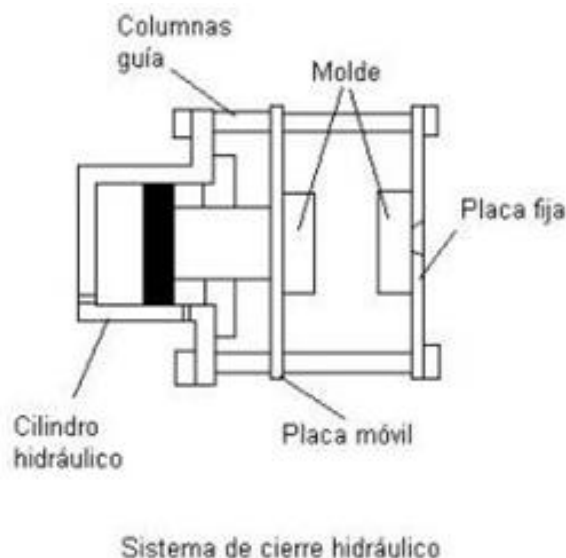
Partes principales que forman el sistema de cierre hidráulico.(Referencia 2)
